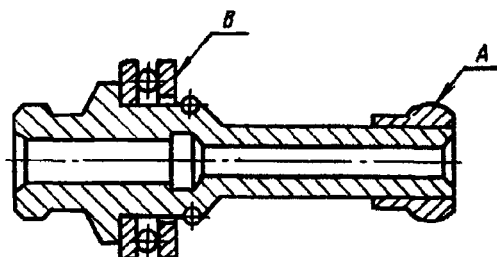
Муфта грузов регулятора с подшипником в сборе
